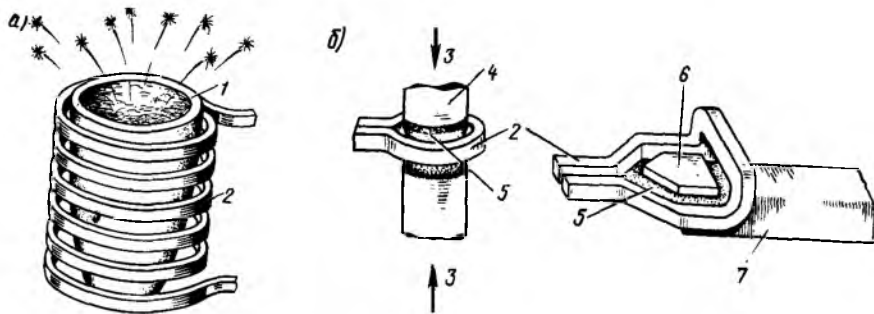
Расплавление металла (а), сварка и пайка (б) металлических деталей с помощью вихревых токов:
